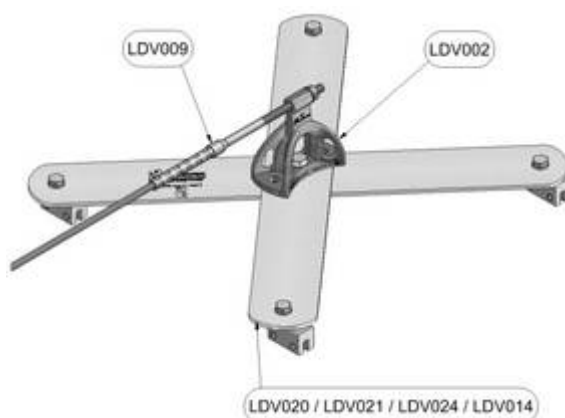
Montage ancre terminale avec bague à sertir à embout fileté sur toiture à joints debout
